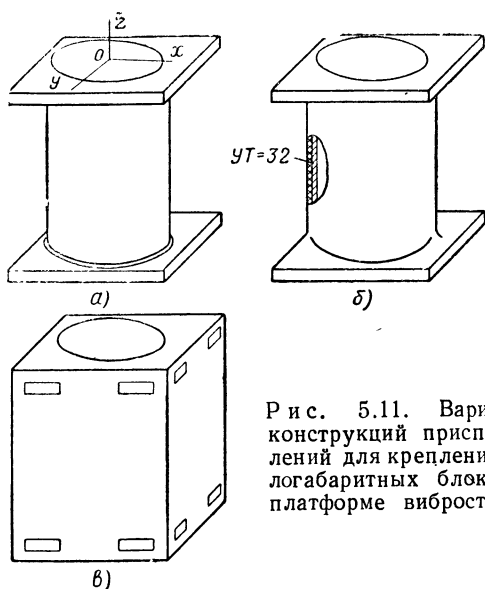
Варианты конструкций приспособлений для крепления малогабаритных блоков к платформе вибростенда.
